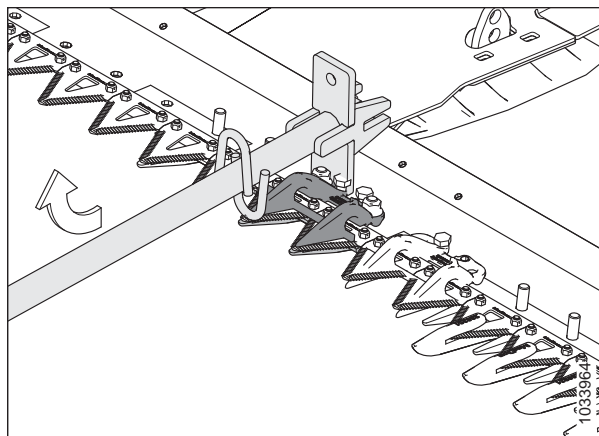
Регулировка смещением вверх — укороченный противорежущий палец
